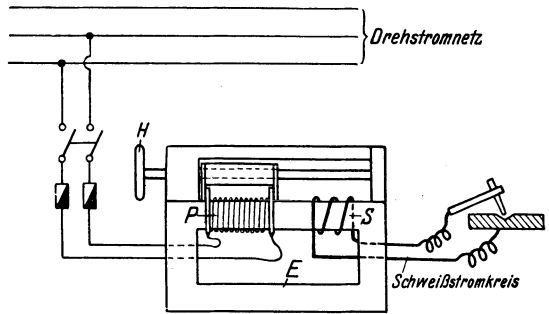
Schweißtransformator mit verschiebbarer Spule.
